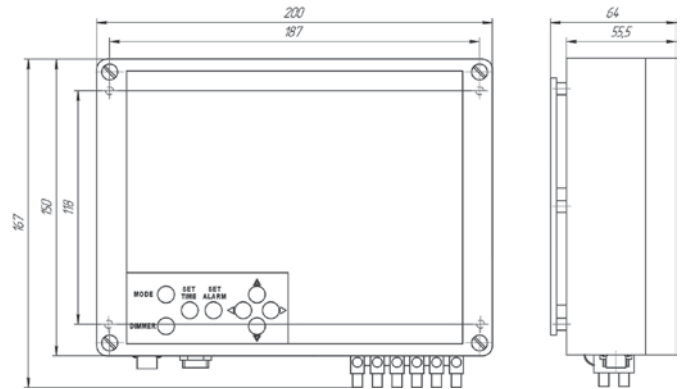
Габаритный чертеж ИПСС-02, ИПСС-03
